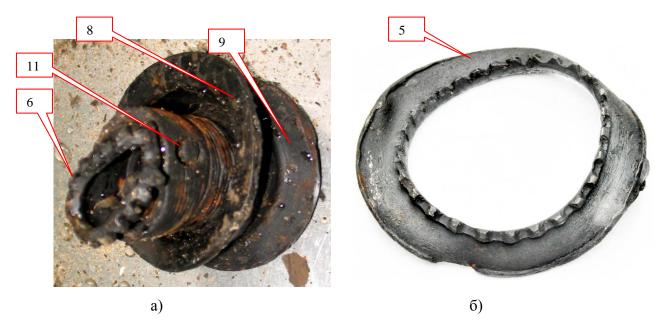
Виды (a, б) деталей узла соединения вала компрессора с валом турбины. Обозначения деталей соответствуют обозначениям на рис. 28.
